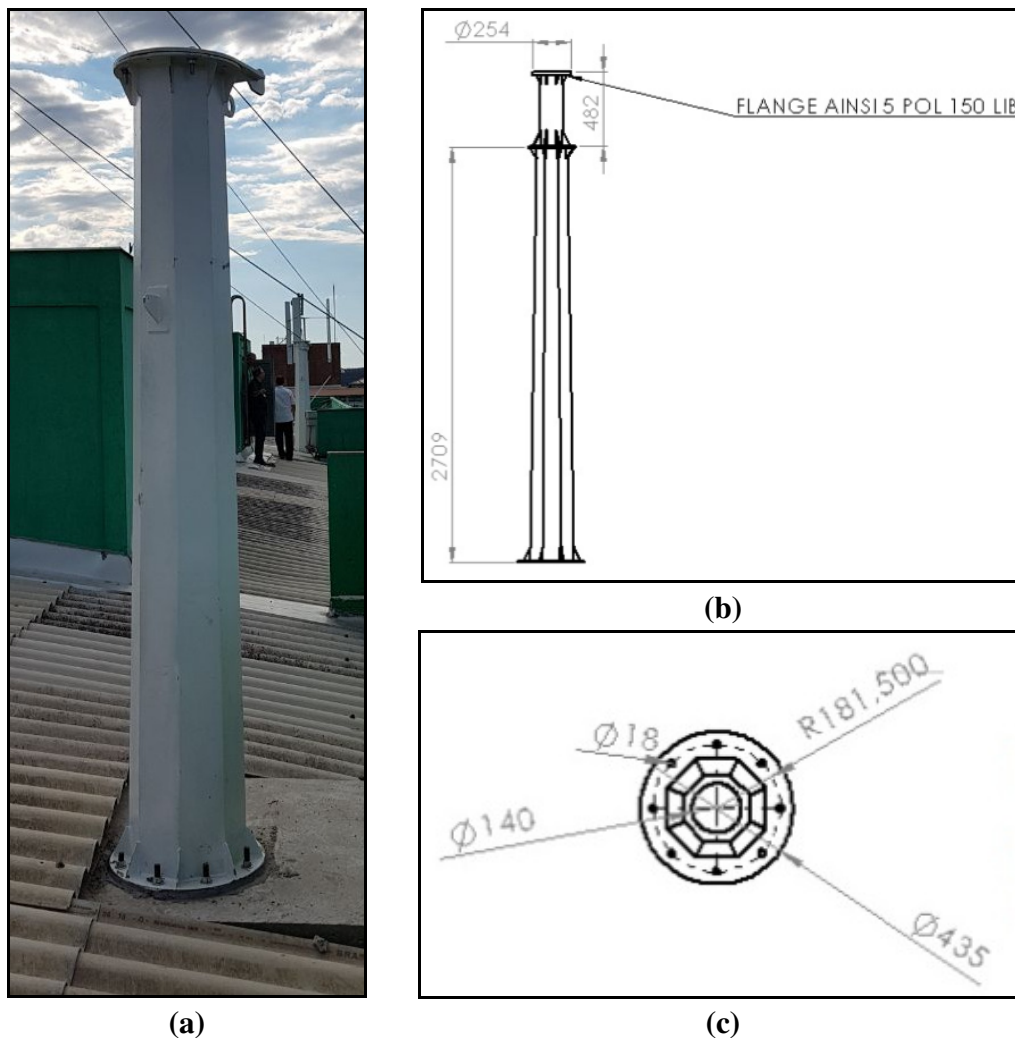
Torre do Aerogerador – (a) Instalada – (b) Desenho dimensional lateral – (c) Desenho dimensional da base
